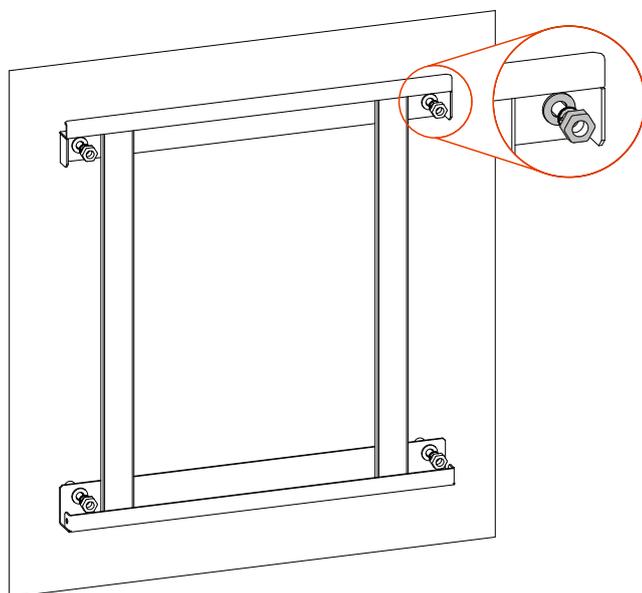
Fissaggio del supporto di installazione sulla parete
